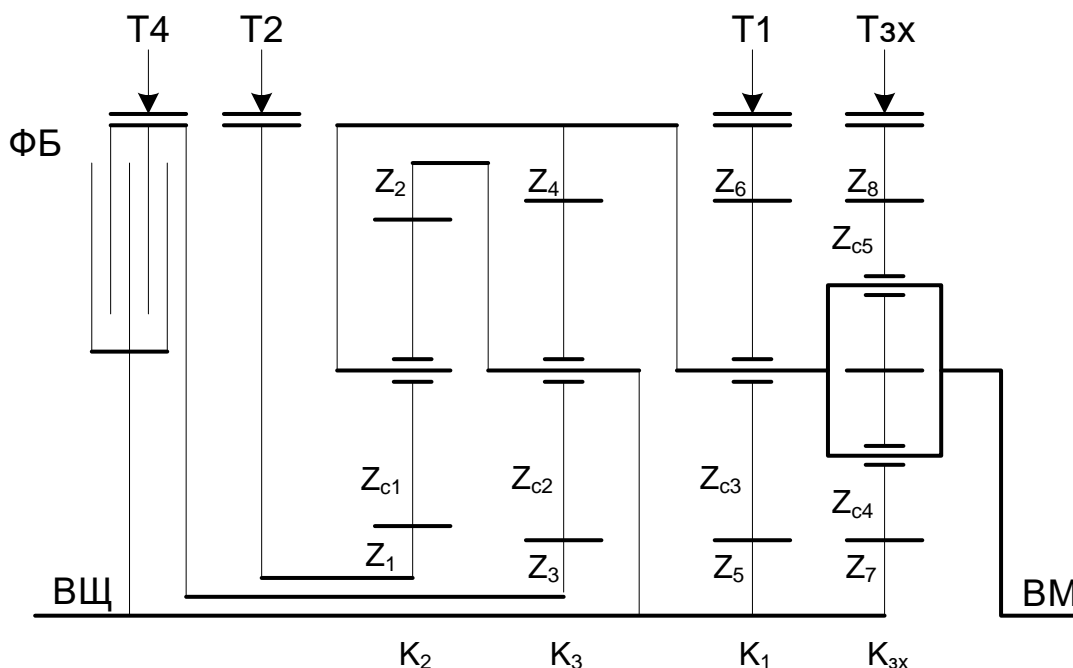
Кинематическая схема планетарной коробки передач типа 4+1
